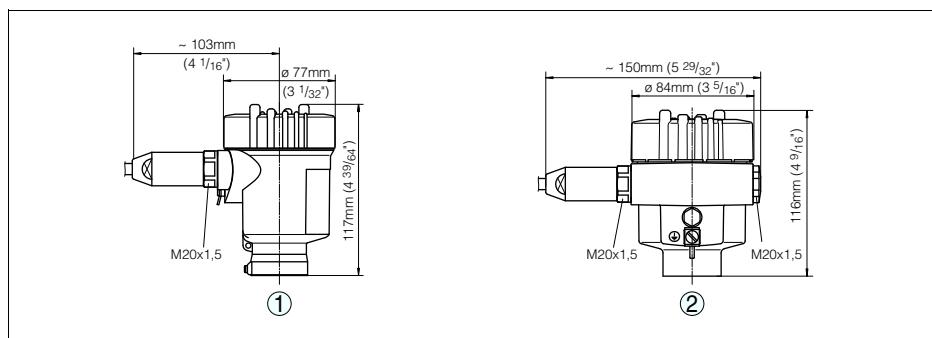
Корпуса в климатическом исполнении IP 66/IP 68, 1 bar (с установленным модулем PLICSCOM корпус выше на 9 мм)
